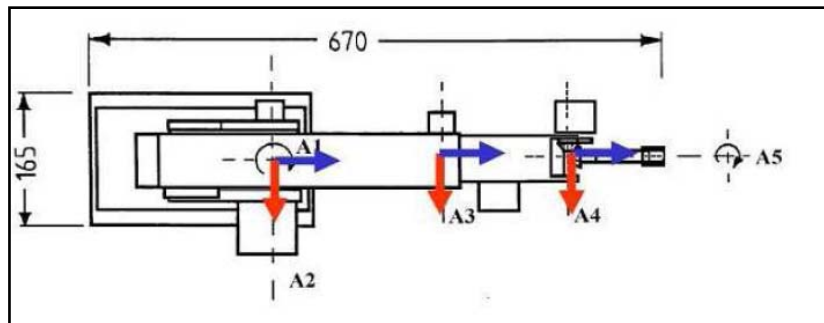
Les dimensions du robot ROB3 (vue de haut).
